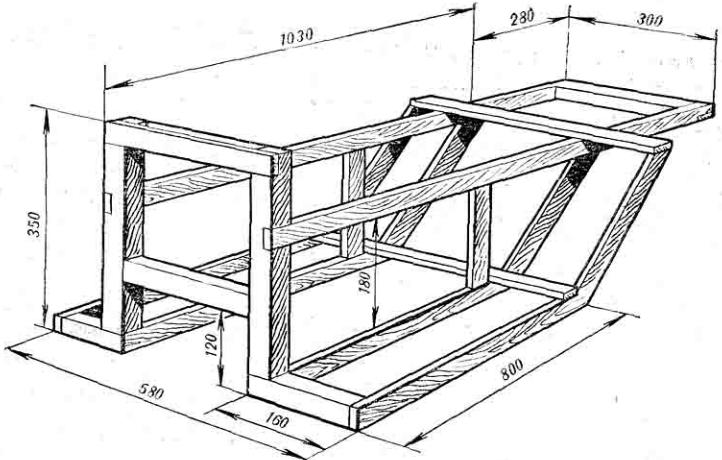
Конструкция каркаса корпуса микромотонарт.
